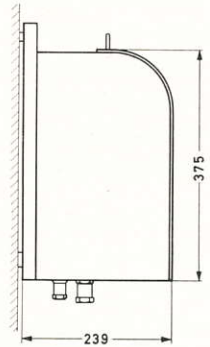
mit Gehäuse für Wandaufhängung 90zTW
